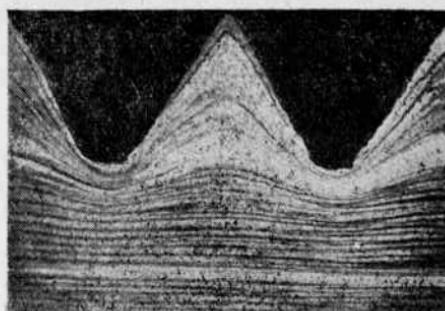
Макрошлиф заготовки с накатанной и нарезанной резьбами.
